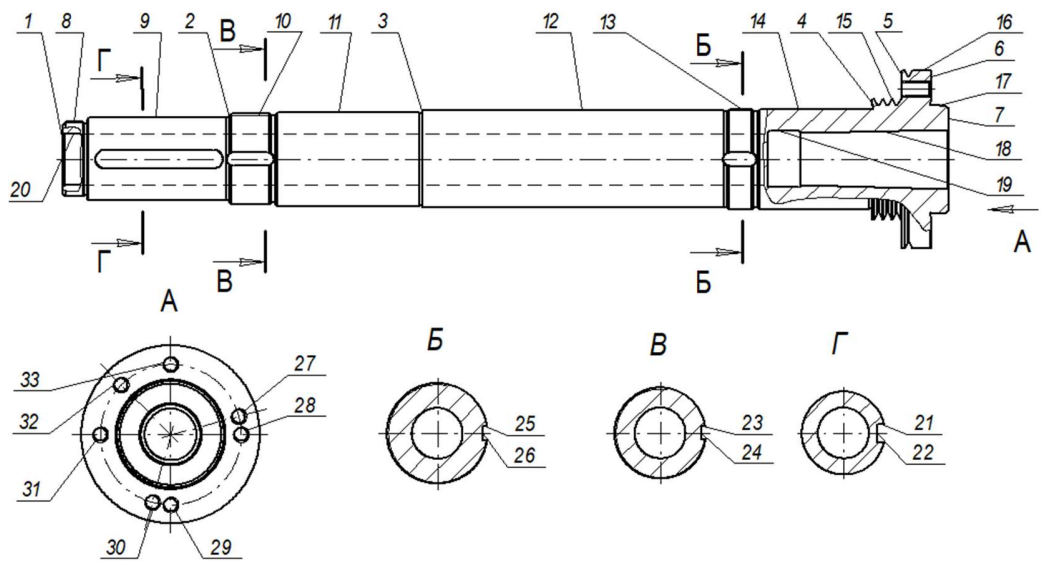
Позначення поверхонь шпинделя для вибору баз
